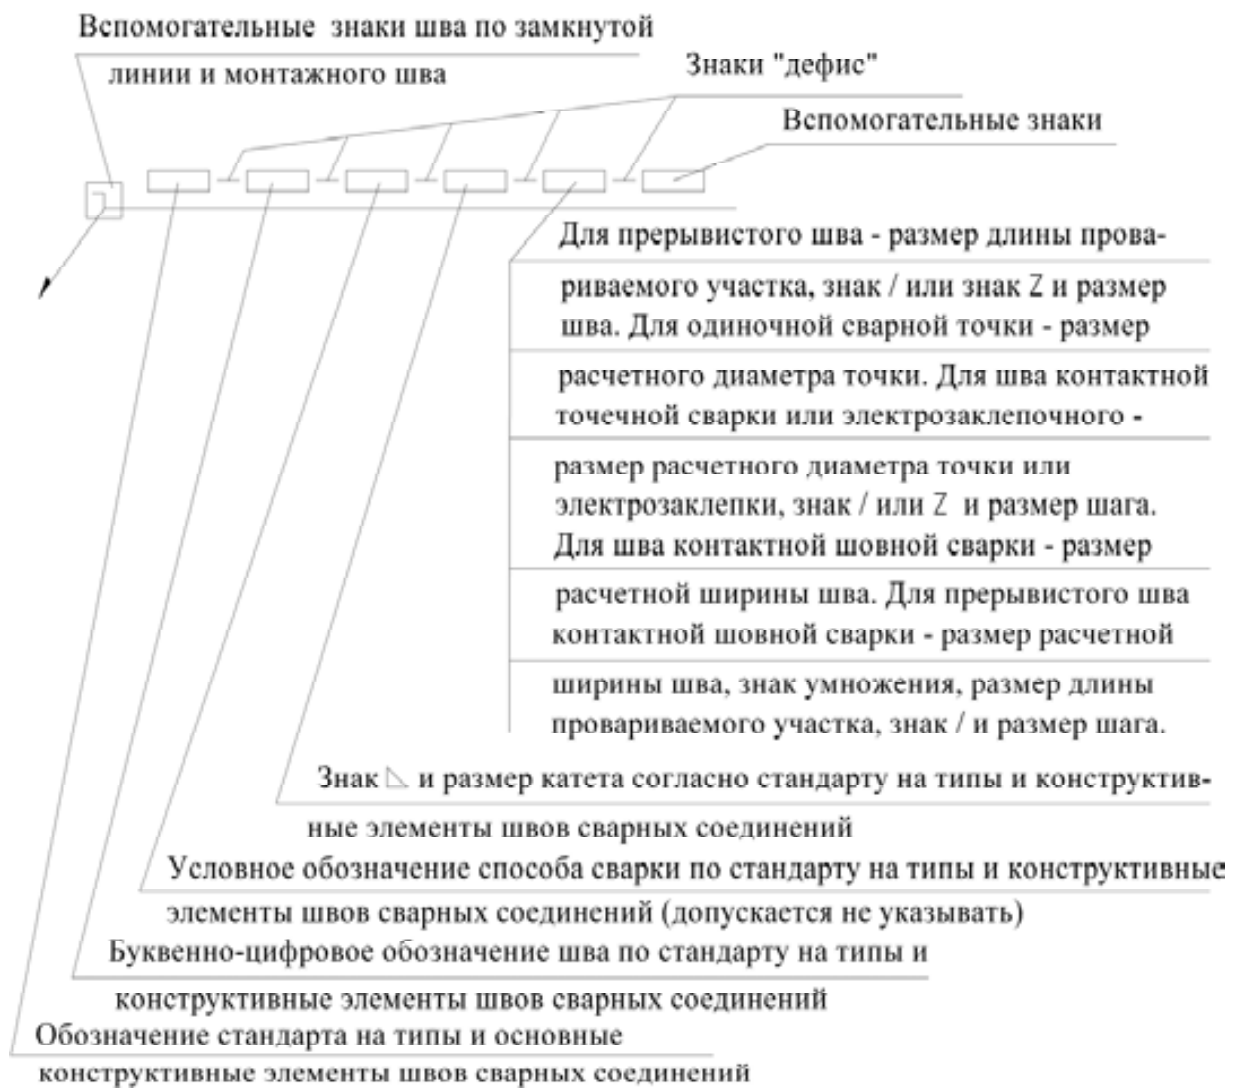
Структура обозначения стандартного сварного шва
